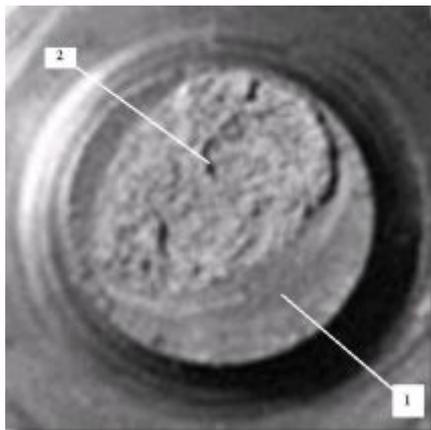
Усталостный излом шпильки крепления крышки турбины: 1 - серповидная усталостная трещина; 2 – зона статического разрушения
